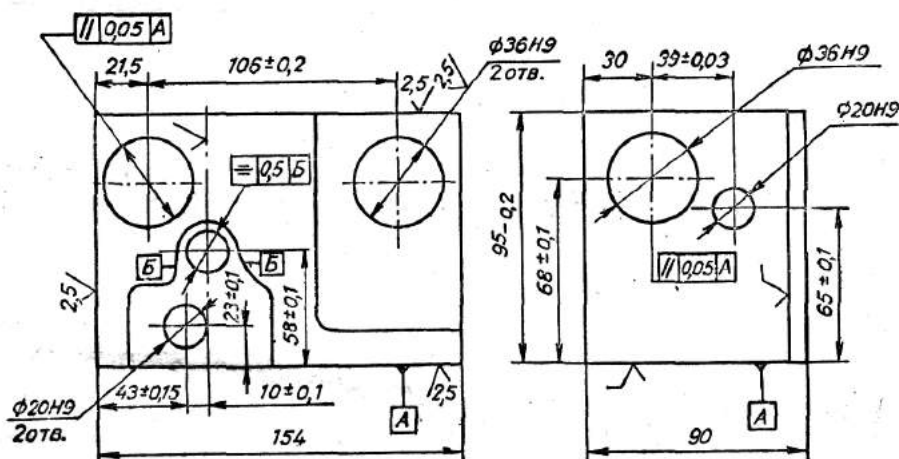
Ескіз корпусу, що обробляється на ГАД.
